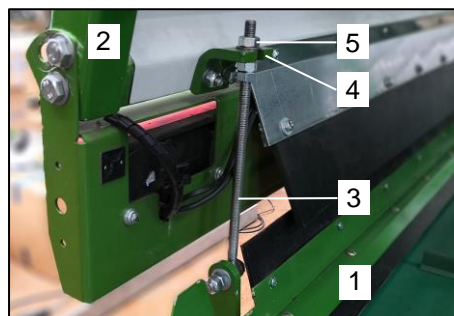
Séparer le convoyeur transversal de la porte arrière
